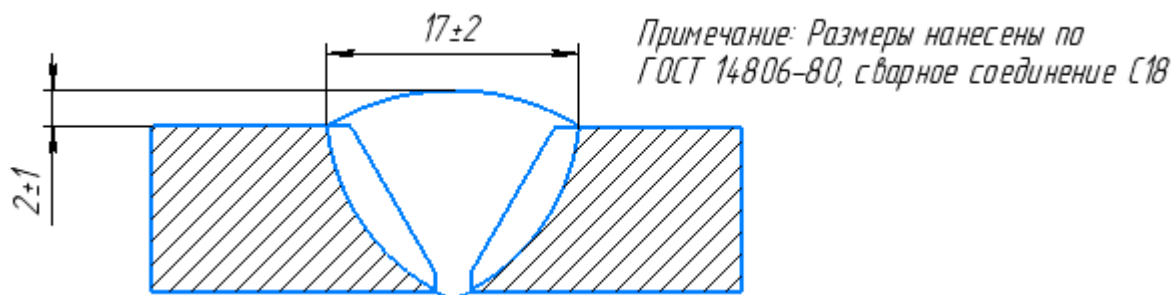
Сварное соединение С18, геометрические размеры сварного шва
